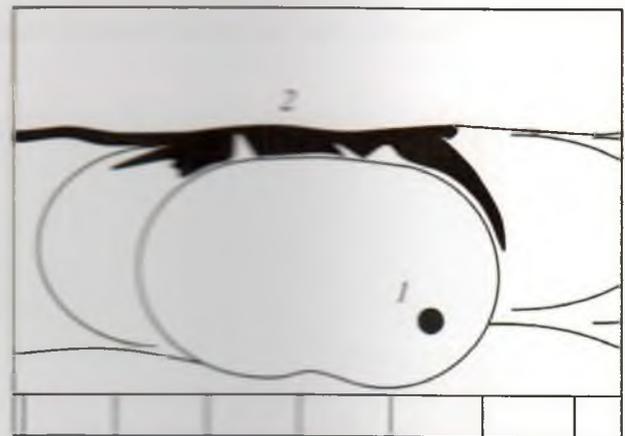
Остроугольное шлаковое включение на поверхности металла стыкового сварного соединения
